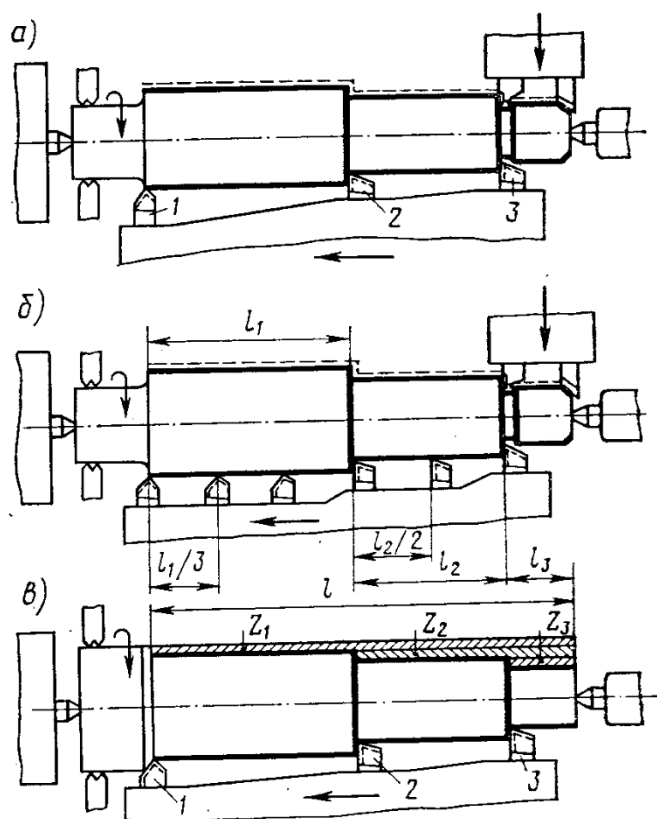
Схемы многорезцового обтачивания заготовок ступенчатых валов
